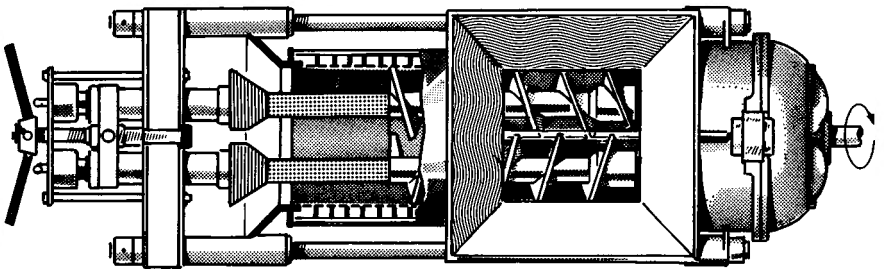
Schnitt durch die Duchscher-Doppel-Schraubenpresse P 9 von 1954. Werkzeugzeichnung (Umzeichnung).
